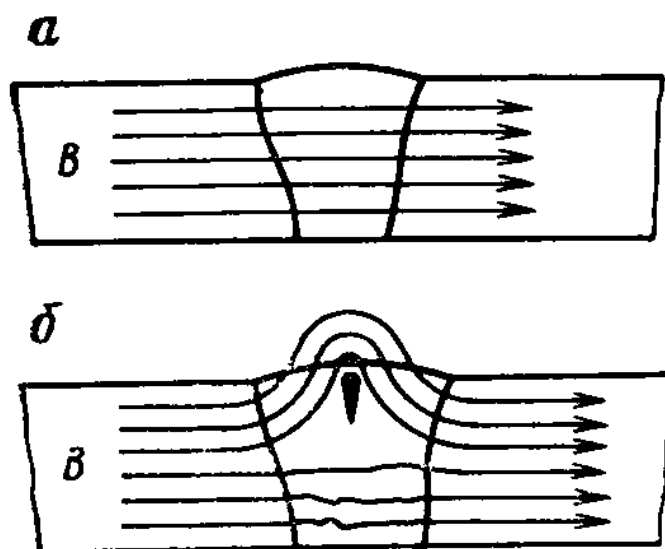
Распределение магнитного потока B по сечению качественного (а) и дефектного (б) сварных швов
